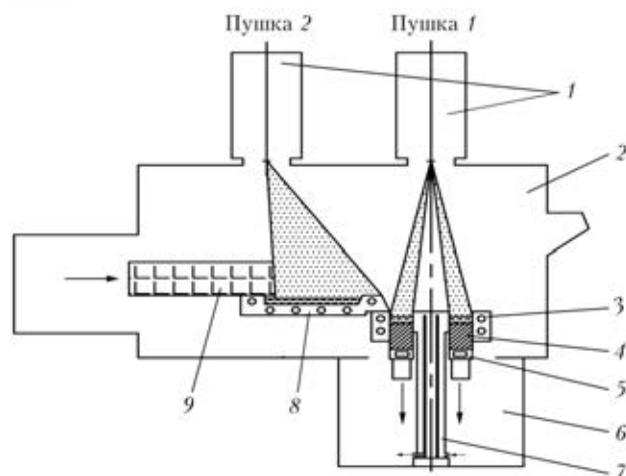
Схема лабораторной установки для получения полого слитка: 1 — электронные пушки; 2 — камера плавки; 3 — кристаллизатор; 4 — полый слиток; 5 — поддон; 6 — камера слитка; 7 — дорн; 8 — промежуточная емкость; 9 — заготовка
